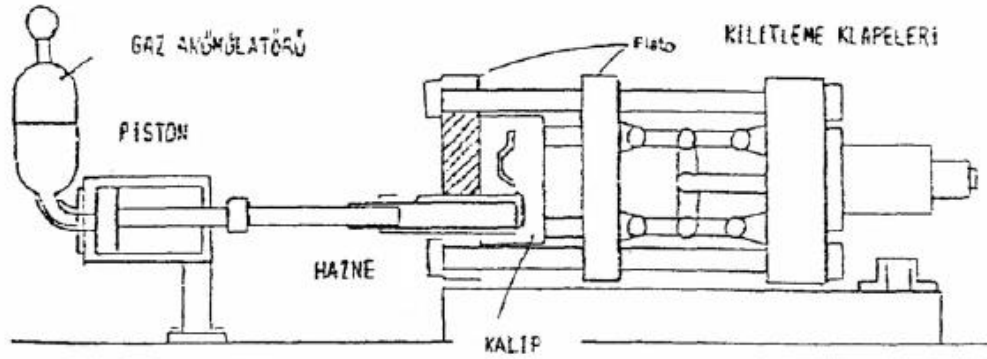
Sıcak Kamaralı Döküm Makinası [5].
